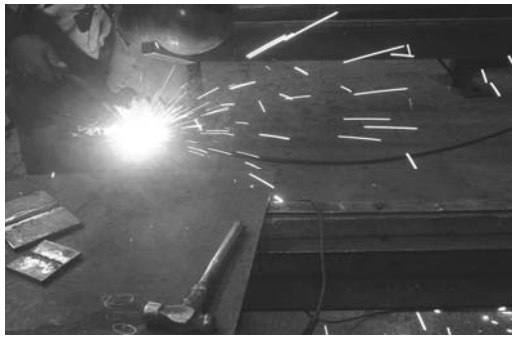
Soldador executando soldagem no aço inoxidável austenítico – 304.
